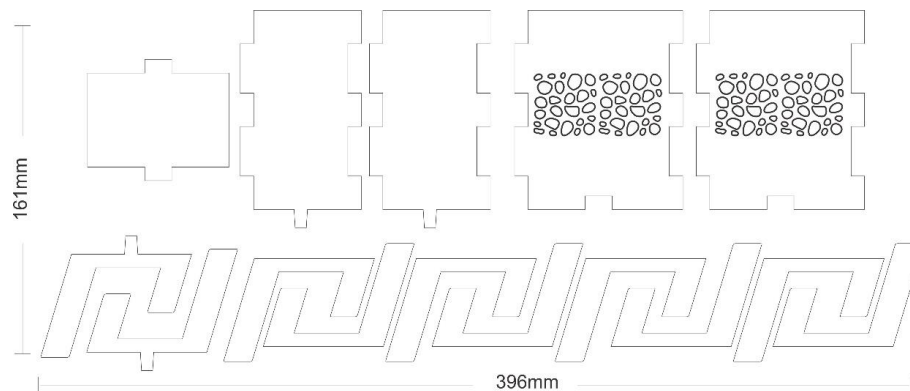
Plano de corte do MDF 6mm do suporte de celular
